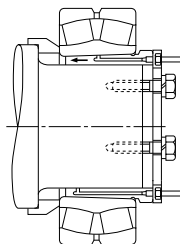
Instalação com Bucha Especial e Pressão Hidráulica
